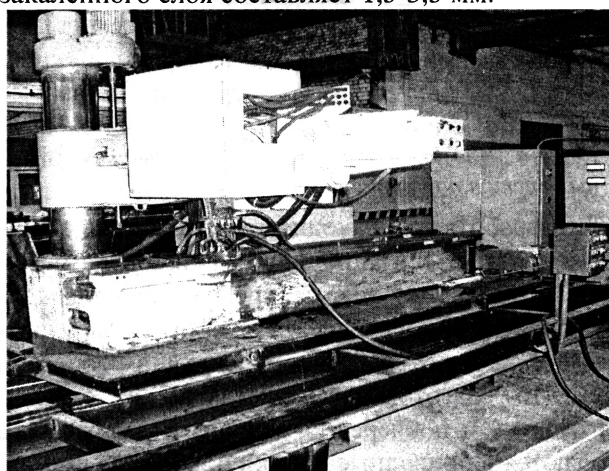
Индукционная установка для закалки ТВЧ направляющих станин металлорежущих станков
